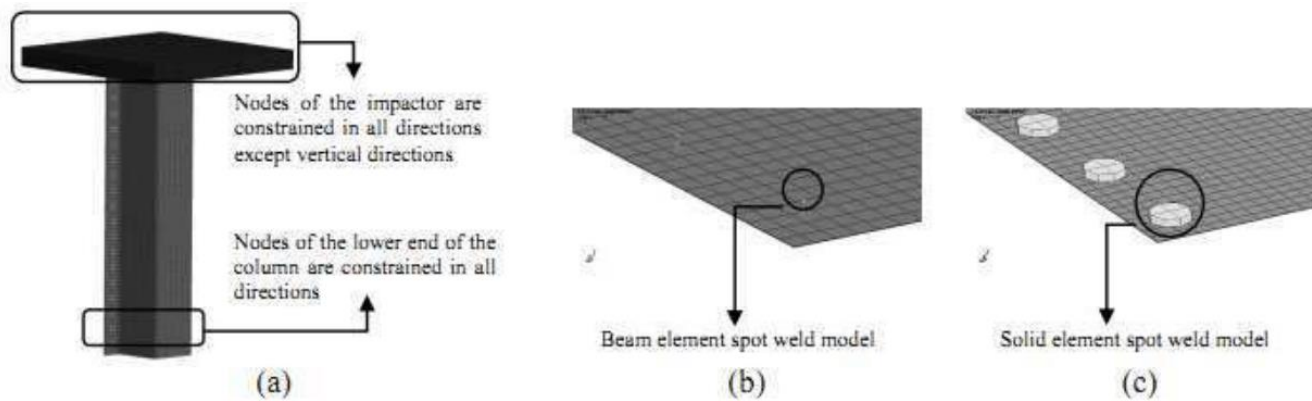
(a) Condiciones de frontera y modelado de puntos de soldadura por elementos (b) 1D y (c) 3D [32].
